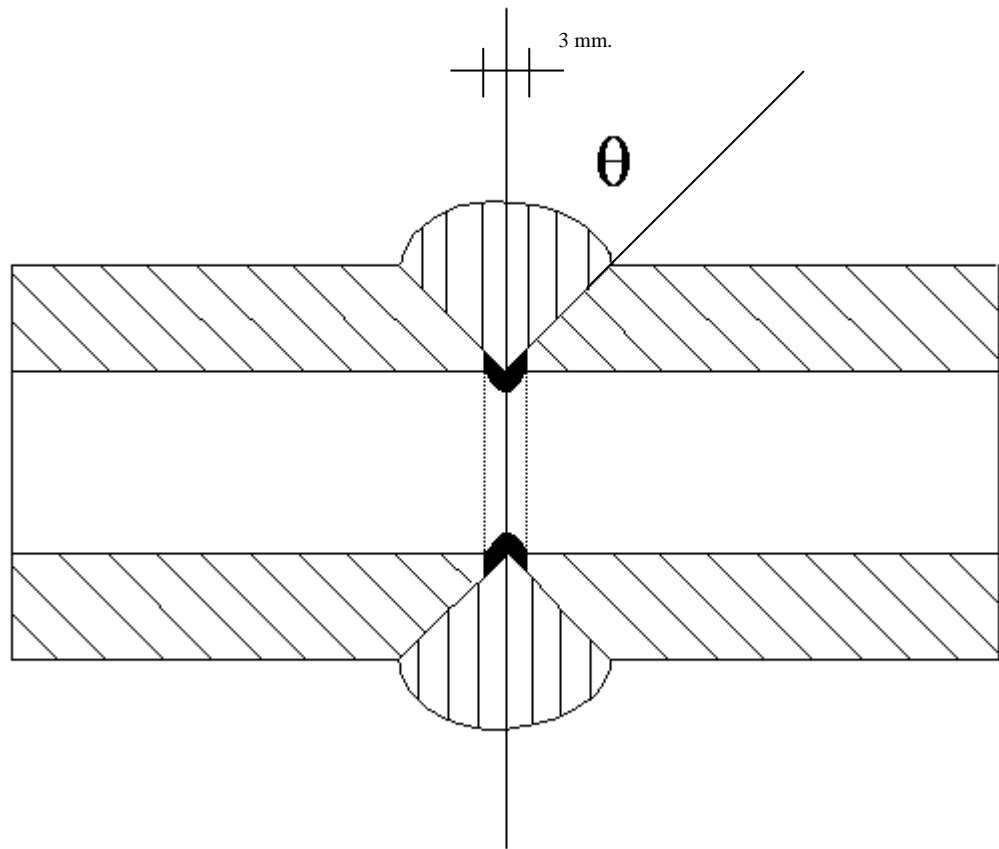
CORDÓN DE SOLDADURA EN UNIÓN DE TUBERÍA
